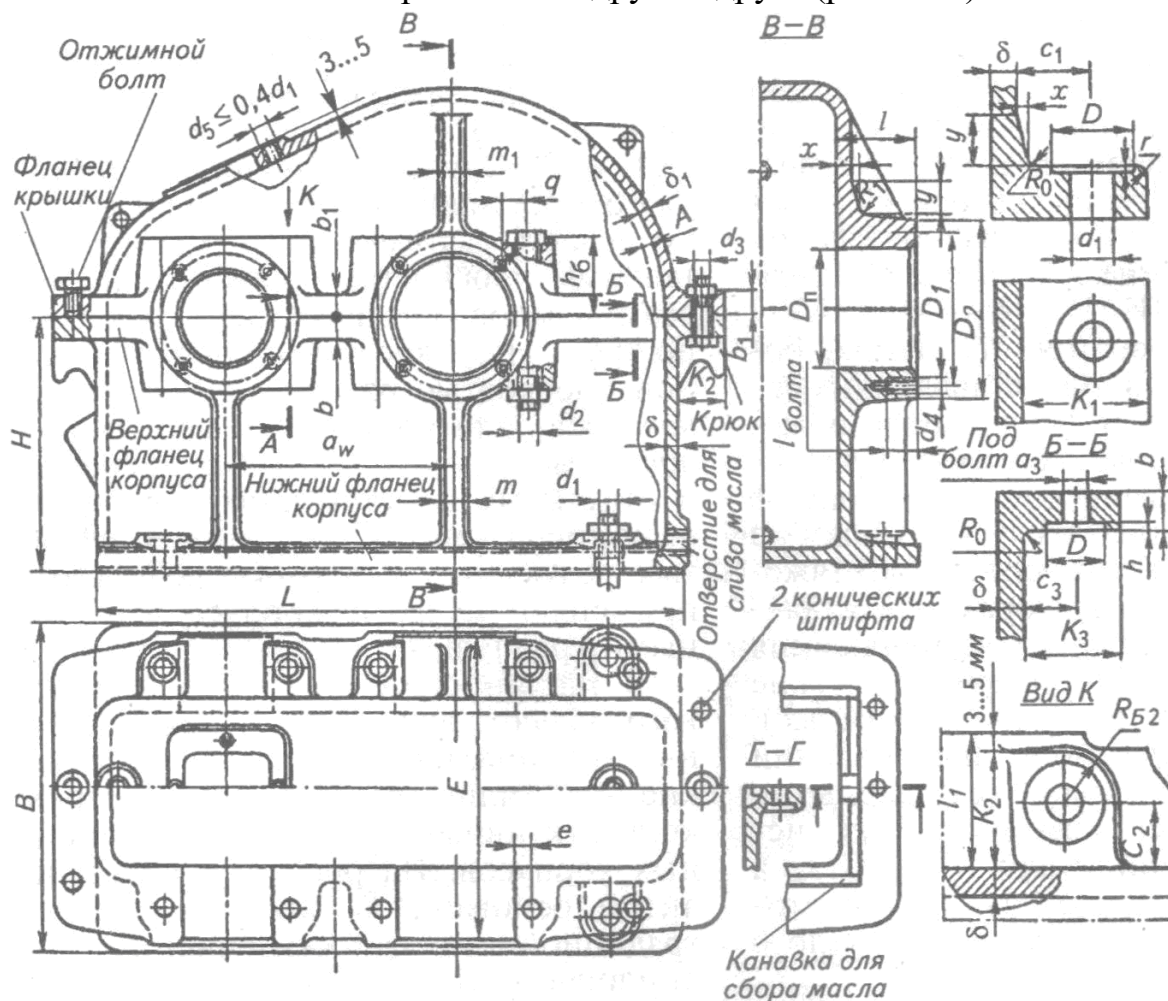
Корпус одноступенчатого цилиндрического редуктора
